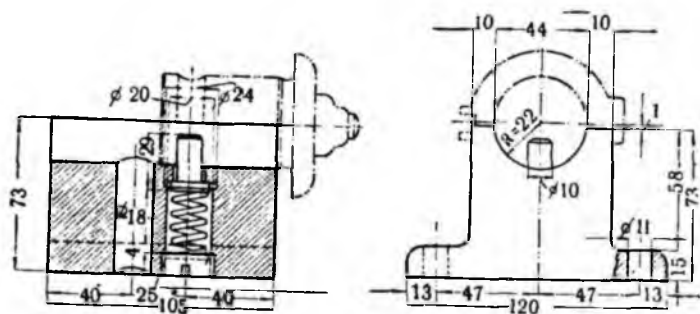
Приспособление для разборки и сборки толкателей насоса ЧТЗ.
